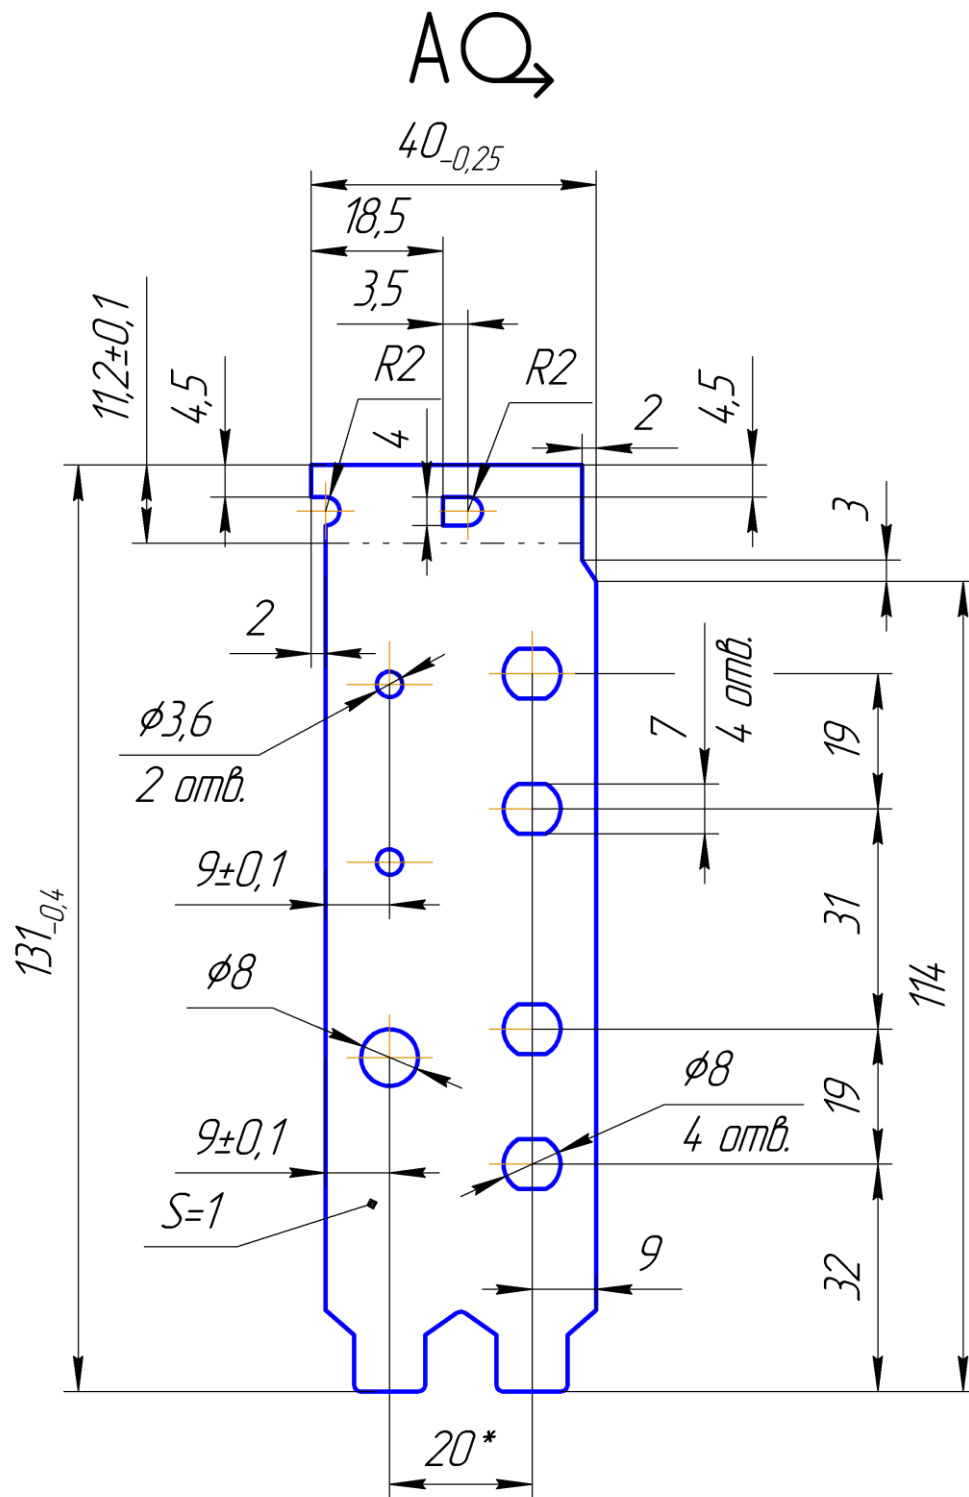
Развертка детали «Планка» с указанием исполняемых размеров
